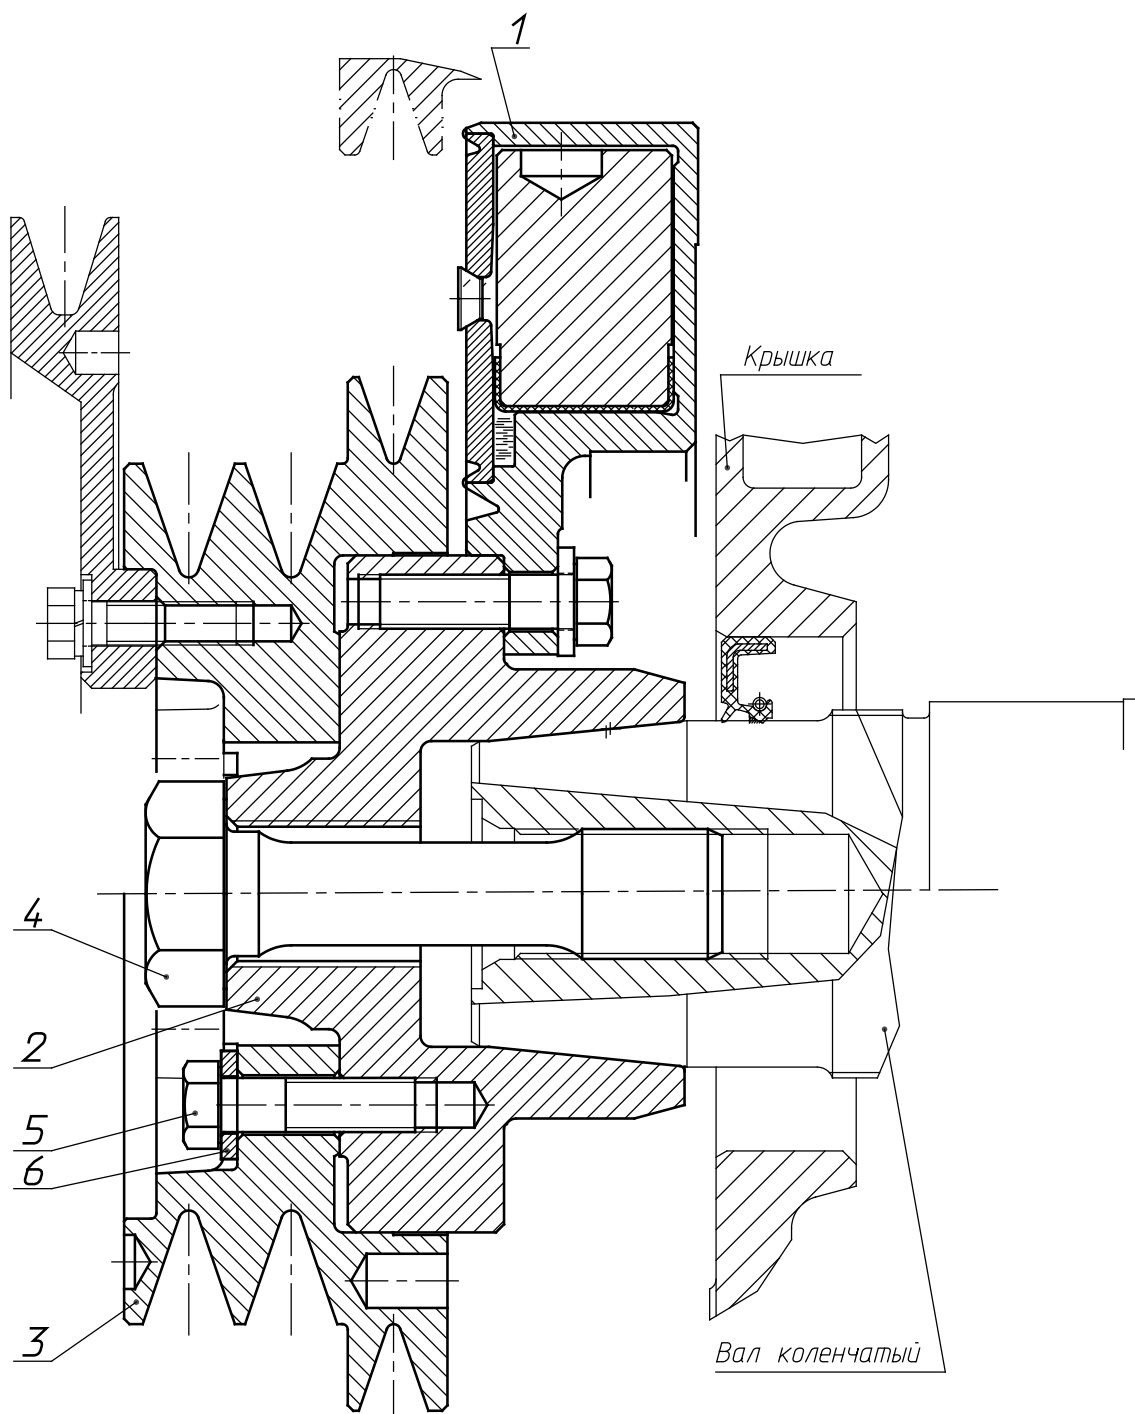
Установка гасителя и шкива на коленчатый вал двигателя типа ЯМЗ-658
